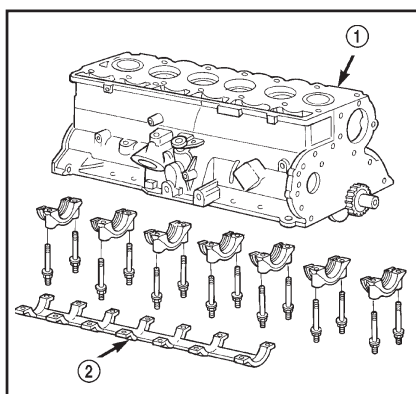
Блок цилиндров двигателя 4,0 л с крышками коренных подшипников и балкой крышек
